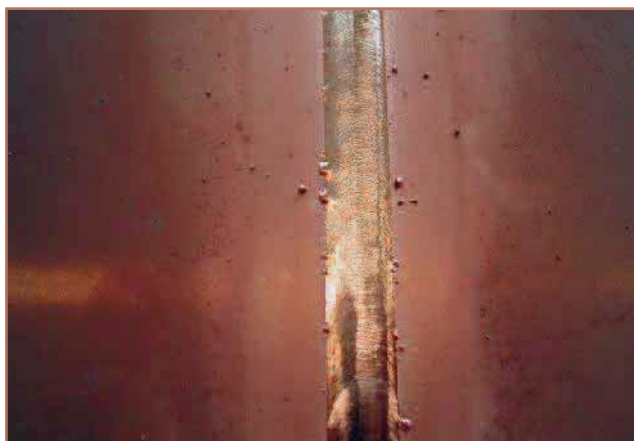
Elektronenstrahlgeschweißtes Kupferblech mit Mehrfokustechnik [65]
